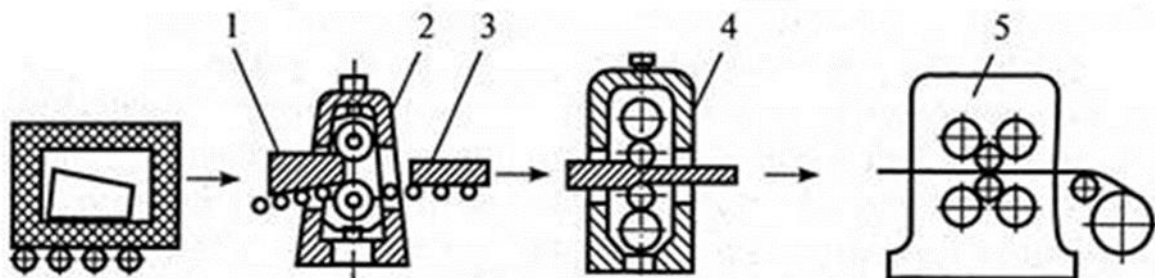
Класична схема виробництва листового прокату: 1 – зливоч; 2 – станок для слябінгу; 3 – сляб; 4 – робоча чорнова кліть; 5 – робоча чистова кліть
